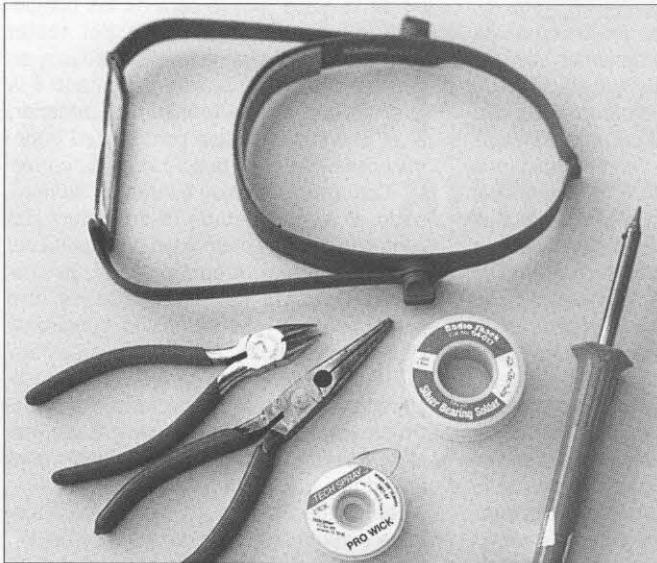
Hay algunas herramientas y accesorios muy útiles que facilitan los montajes propios, como el soldador de bajo vataje, el estaño de aleación de plata, la cinta desoldadora para corregir errores y una lupa magnificadora «ojos mágicos».
